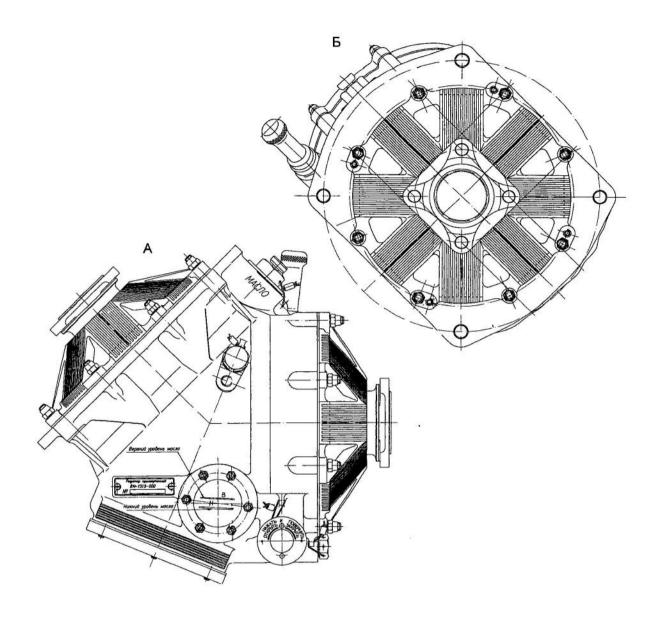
(Лист 2 из 3) Редуктор промежуточный
